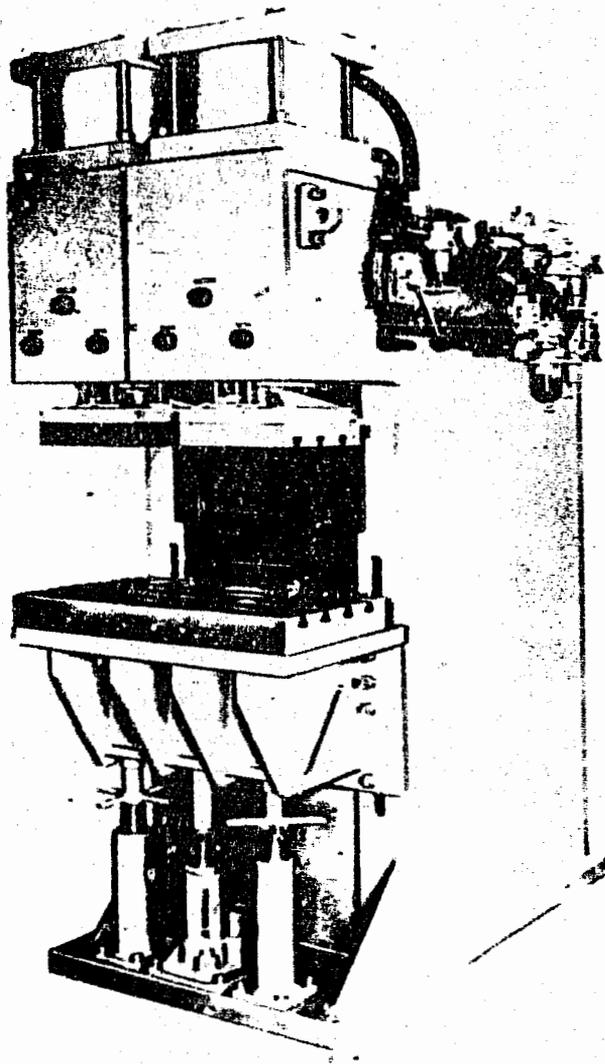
Máquina estacionaria para soldadura por proyección, con doble cabezal.
